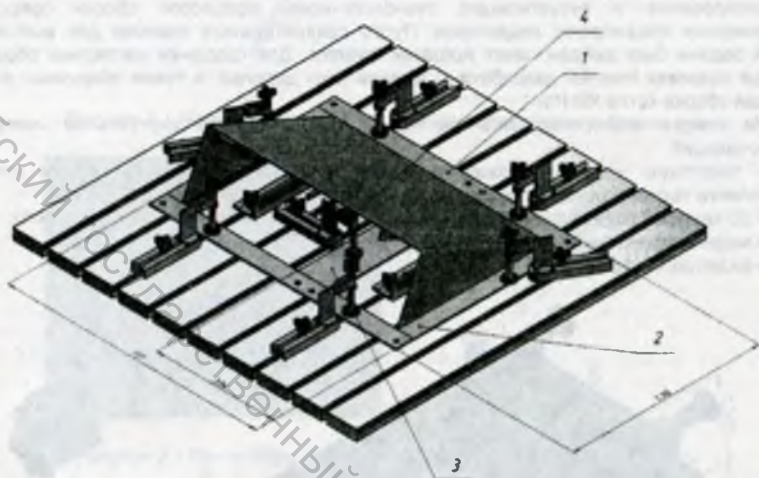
Модель кожуха котла KV-PM-1 в сборочном приспособлении
